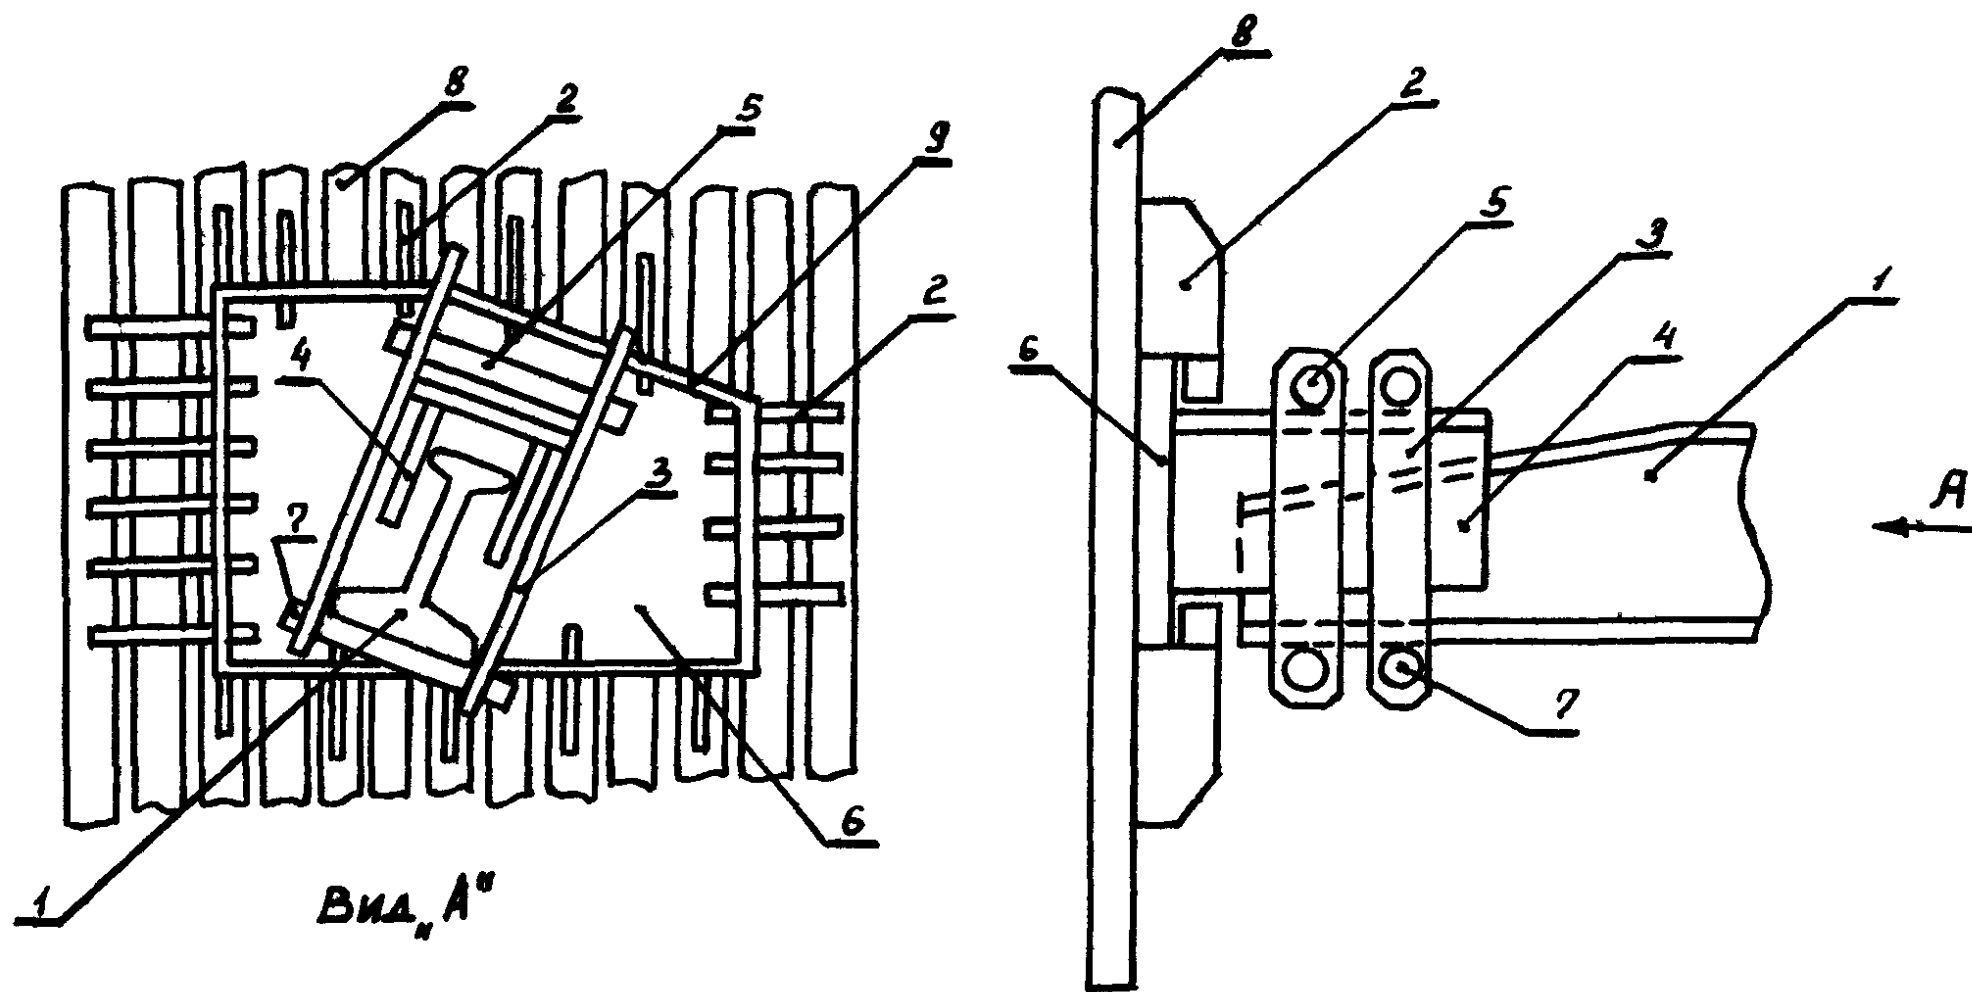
Узел крепления опорной балки к боковым экранным трубам
